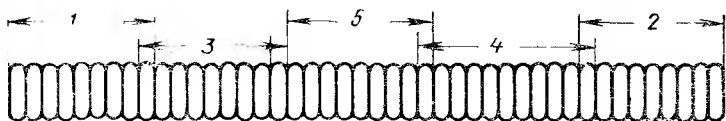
Сварочный шов, наложенный обратно-ступенчатым способом
